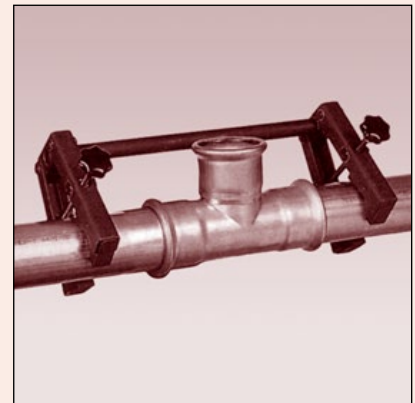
| Verwendung des Rohrschraubstocks für Durchmesser "Big Size"
